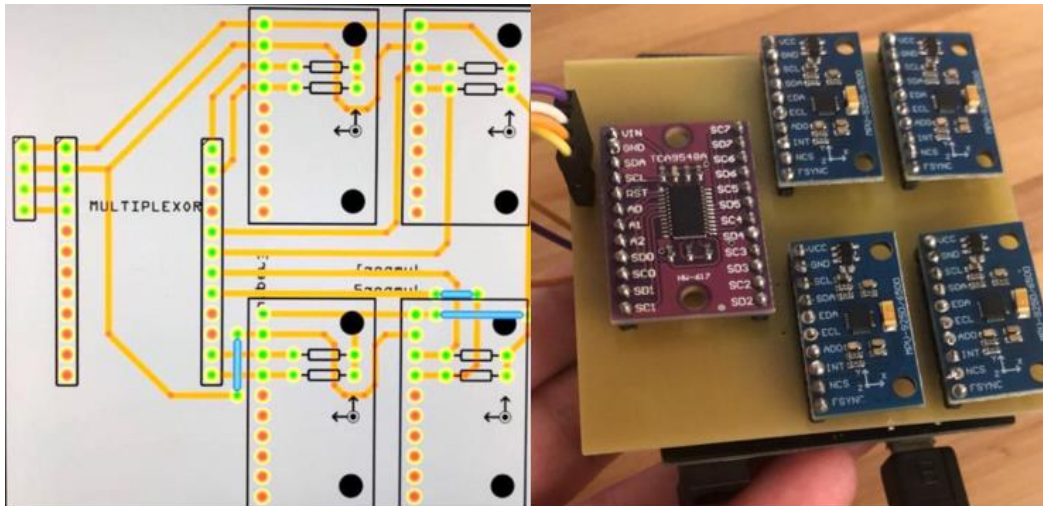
Esquemático de la PCB diseñada en Fritzing (izquierda) y el dispositivo fabricado (derecha)
